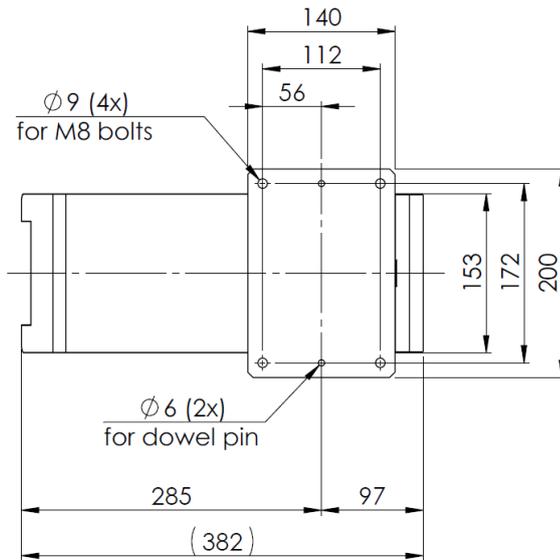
Sockelplatte - Befestigungs- und Positionierbohrungen
